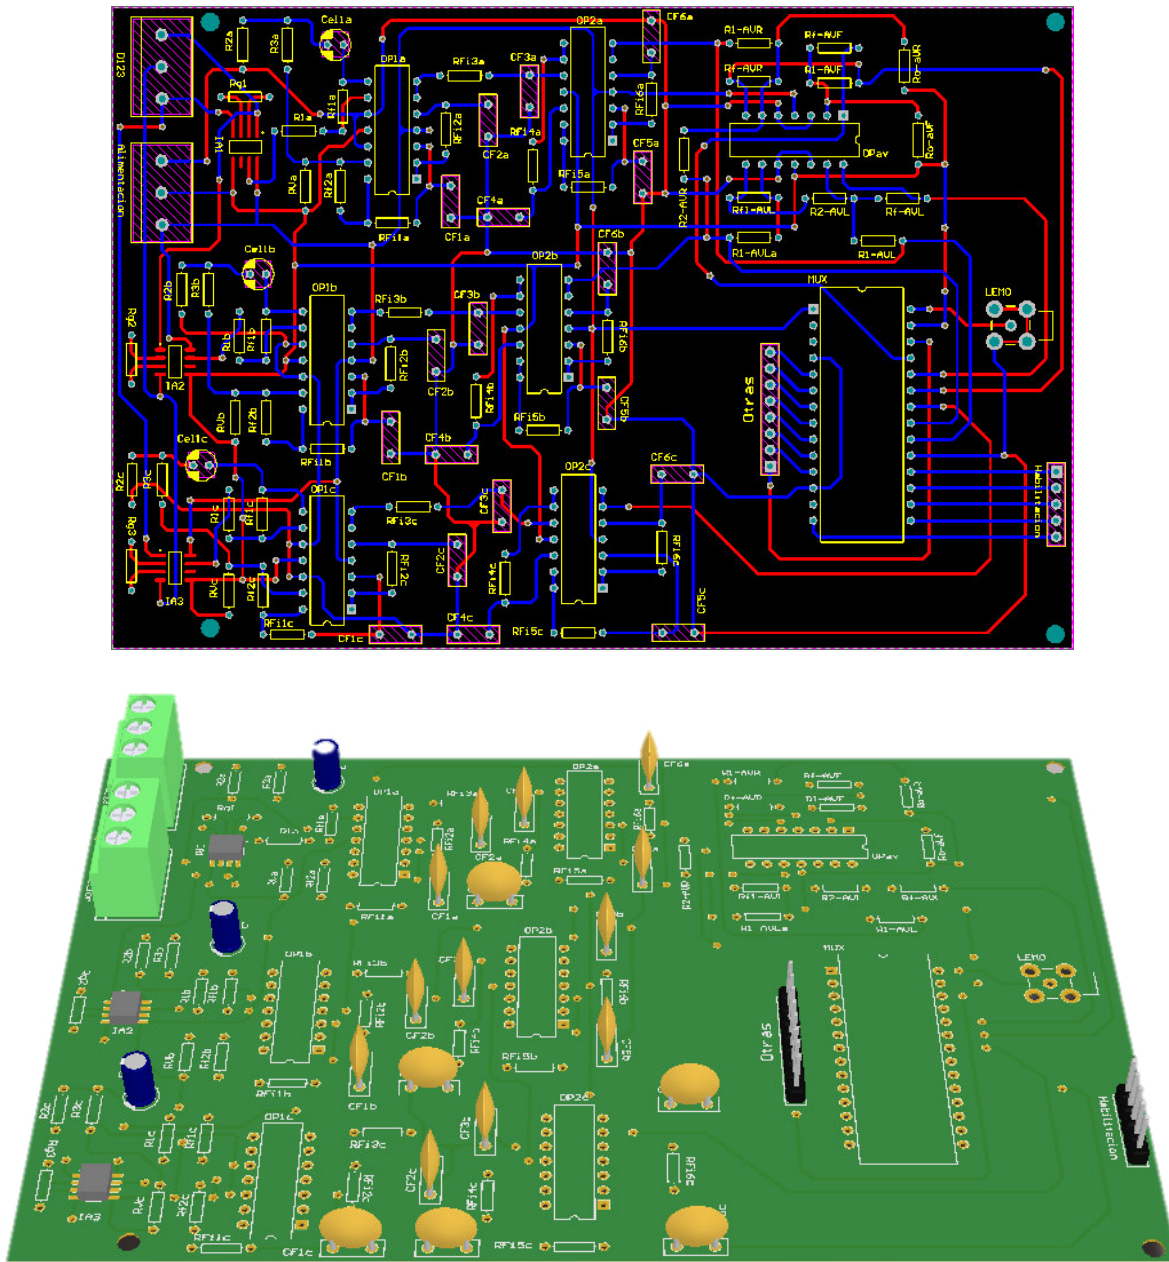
PCB diseñado en Altium para obtener 6 señales del ECG.
